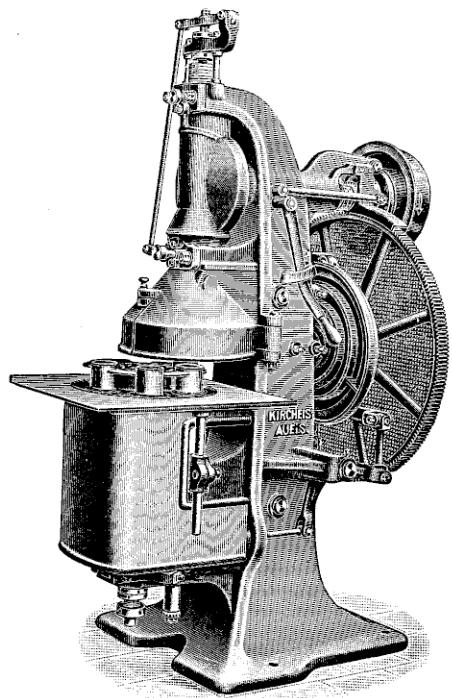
Machine à double-sertir les boîtes de conserves.
